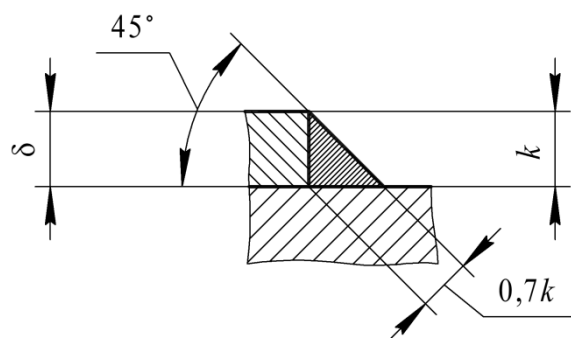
Геометрические параметры углового сварного шва
